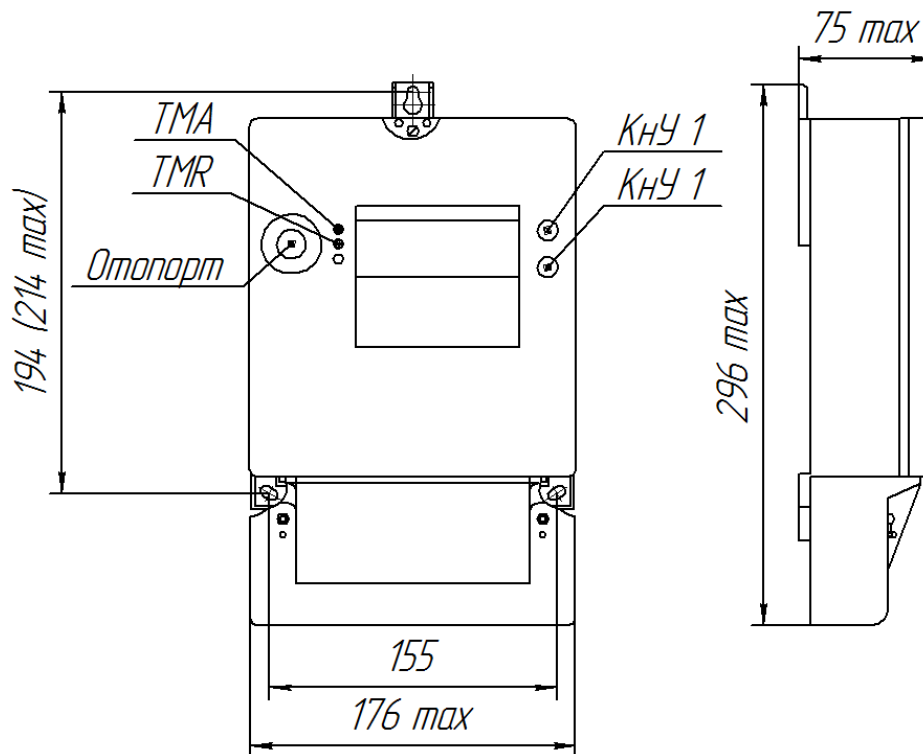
Габаритные, установочные размеры и расположение индикаторов счетчиков
